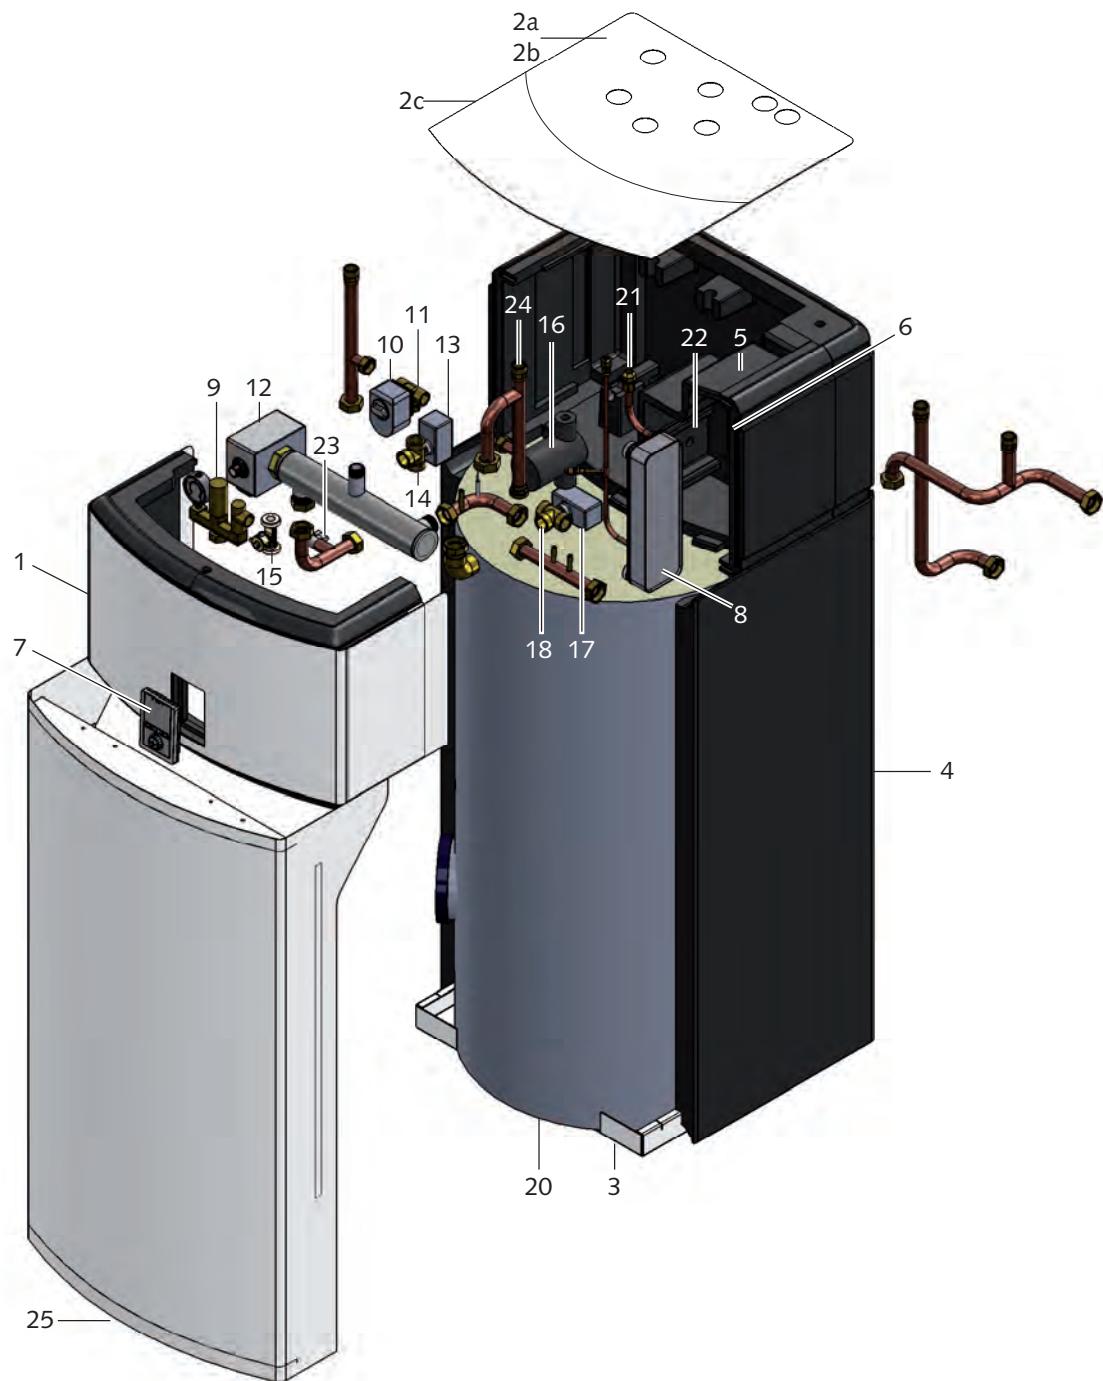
Explosionszeichnung Innenmodul WKF-compact 85/120/180
